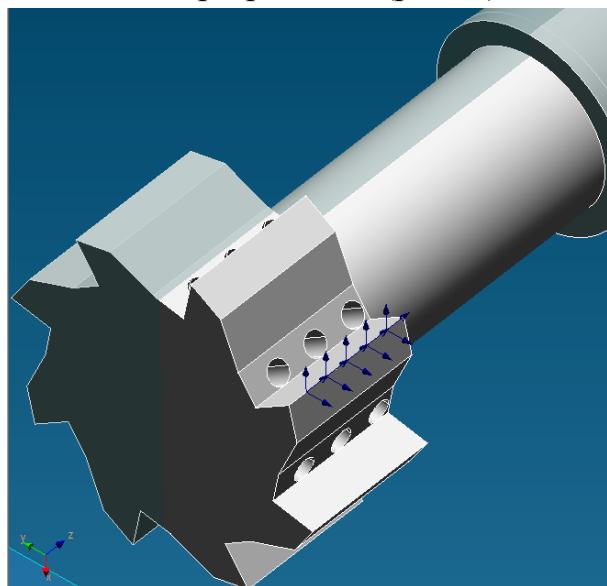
3D-модель Т-образной фрезы с осевым и радиальными каналами для подачи СОТС
